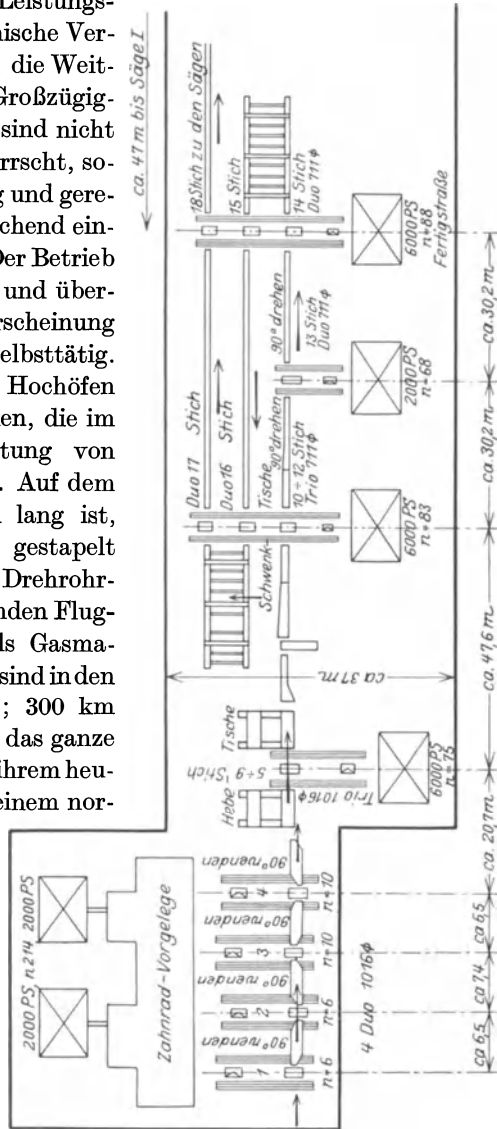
Gary, Grundriß der Block- und Schienenstraße.
